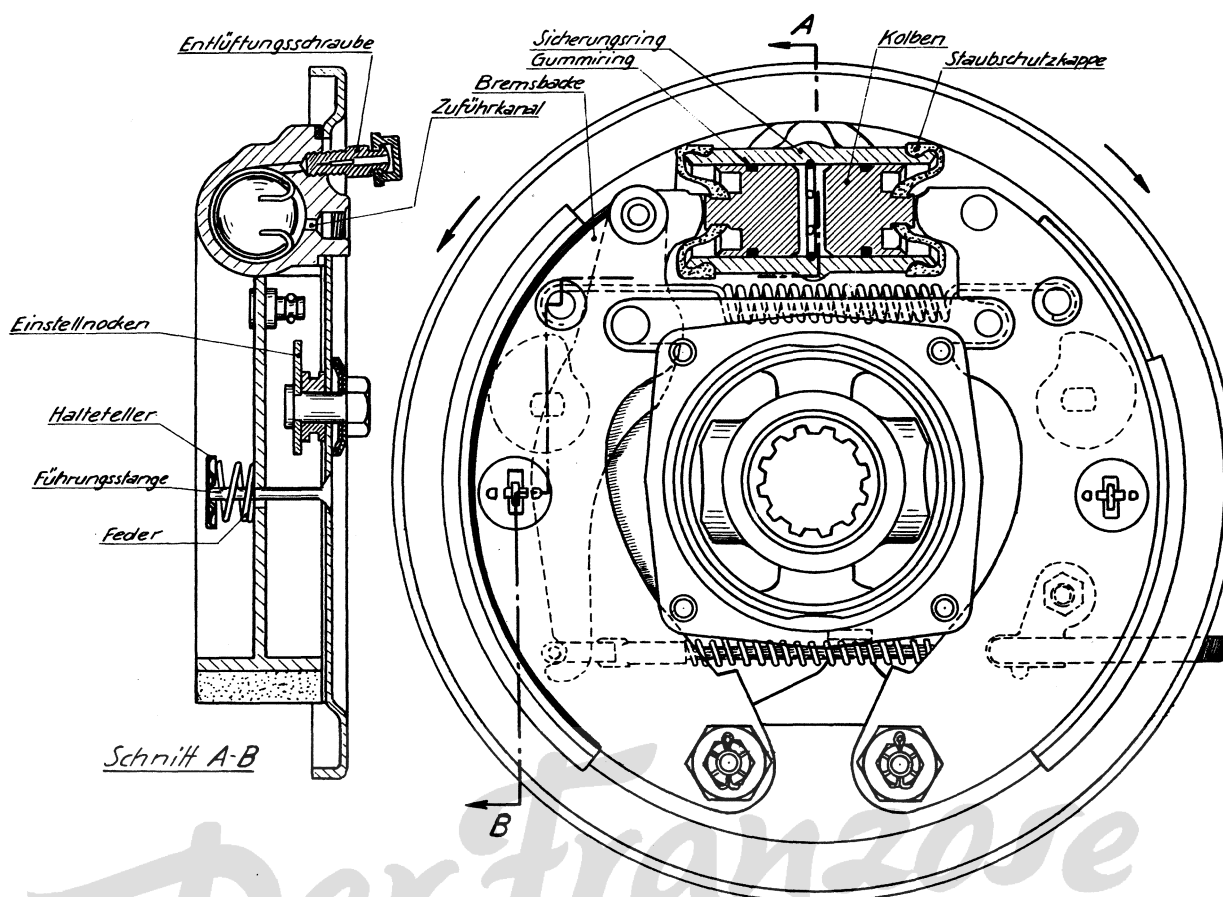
Ansicht und Schnitt der Bremsträgerplatte
